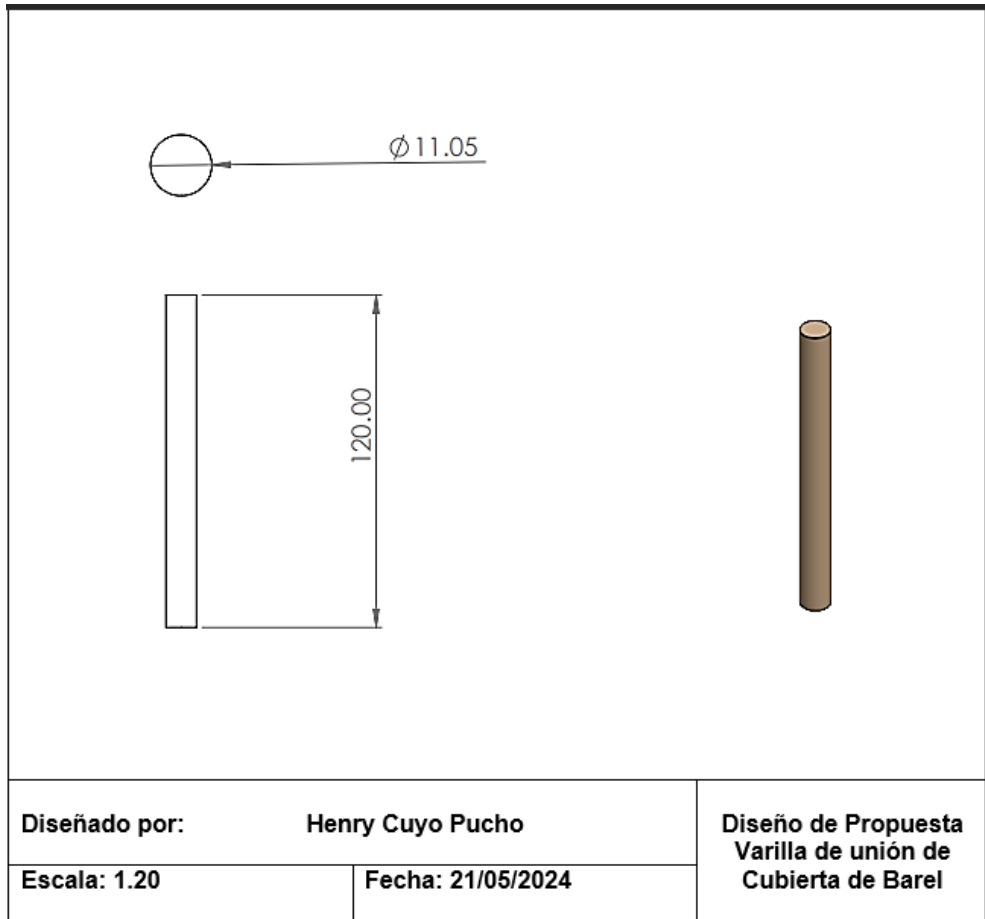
Plano de varilla para armado de Covered Base for Barel -CBB.
